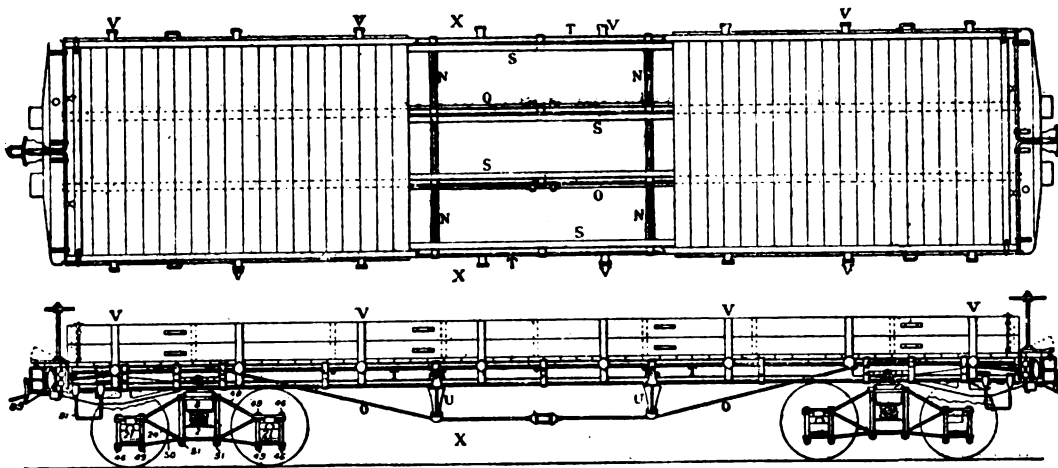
e 16 — Carro a sponde basse tubulare — Elevazione e pianta.
